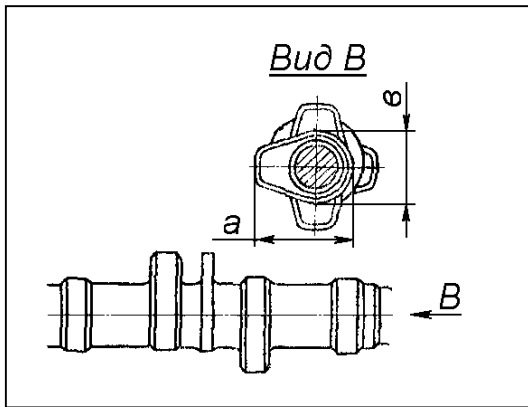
К контролю высоты кулачка кулачкового вала: а – размер от затылка до вершины кулачка; в – диаметр цилиндрической части кулачка.
